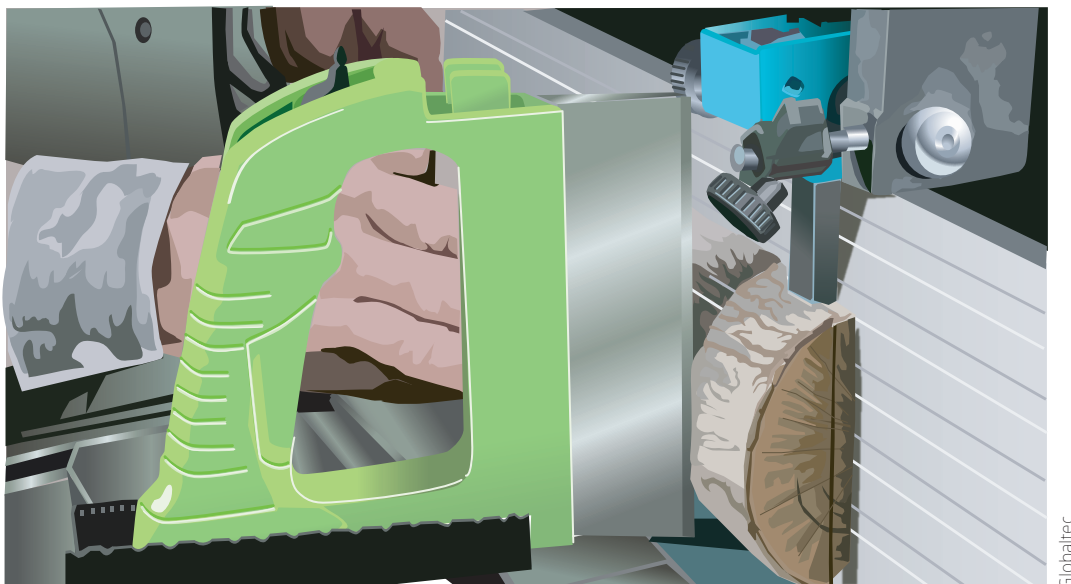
Exemplo de dispositivo auxiliar para cortes especiais
